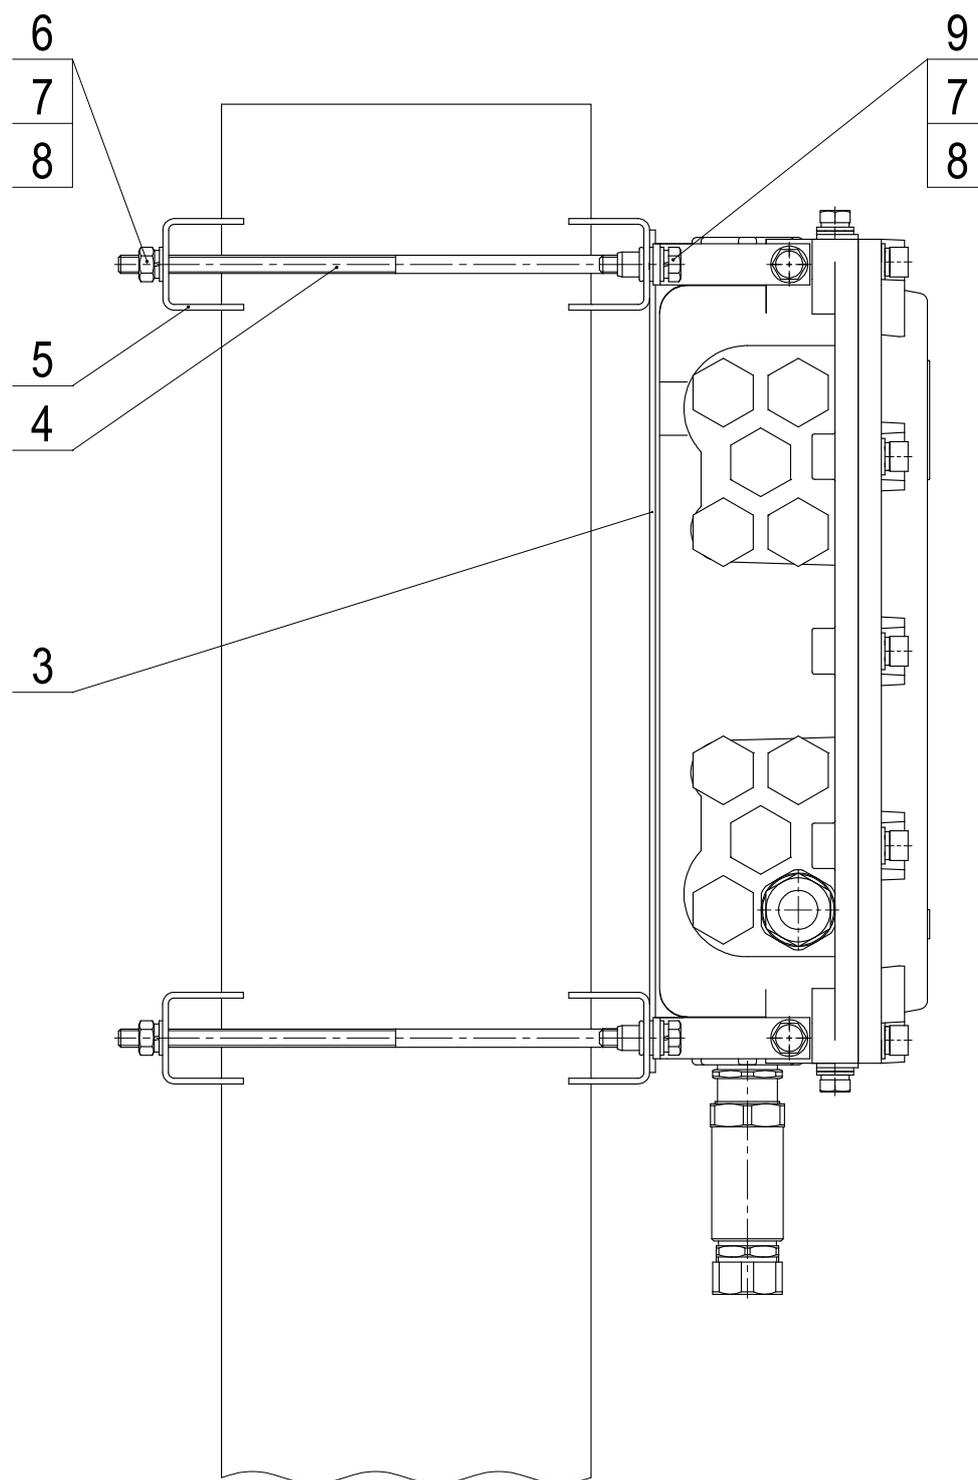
(лист 2 из 2) – Крепление БЭ на ограждении из железобетонных плит или кирпичной стене
